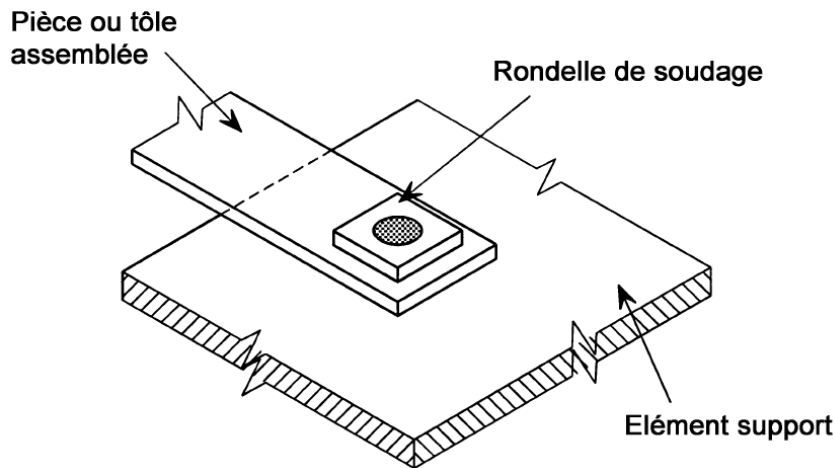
Soudure bouchon à l'arc avec rondelle de soudage
